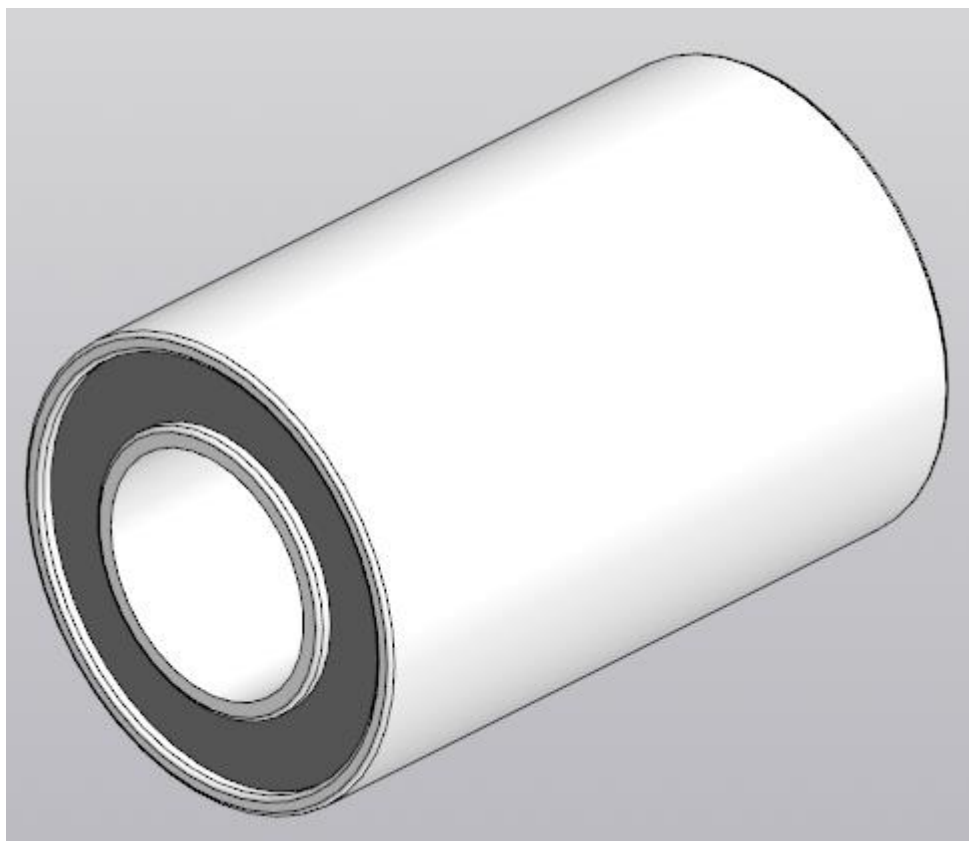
3D-модель лінійного підшипника LM10UU.
